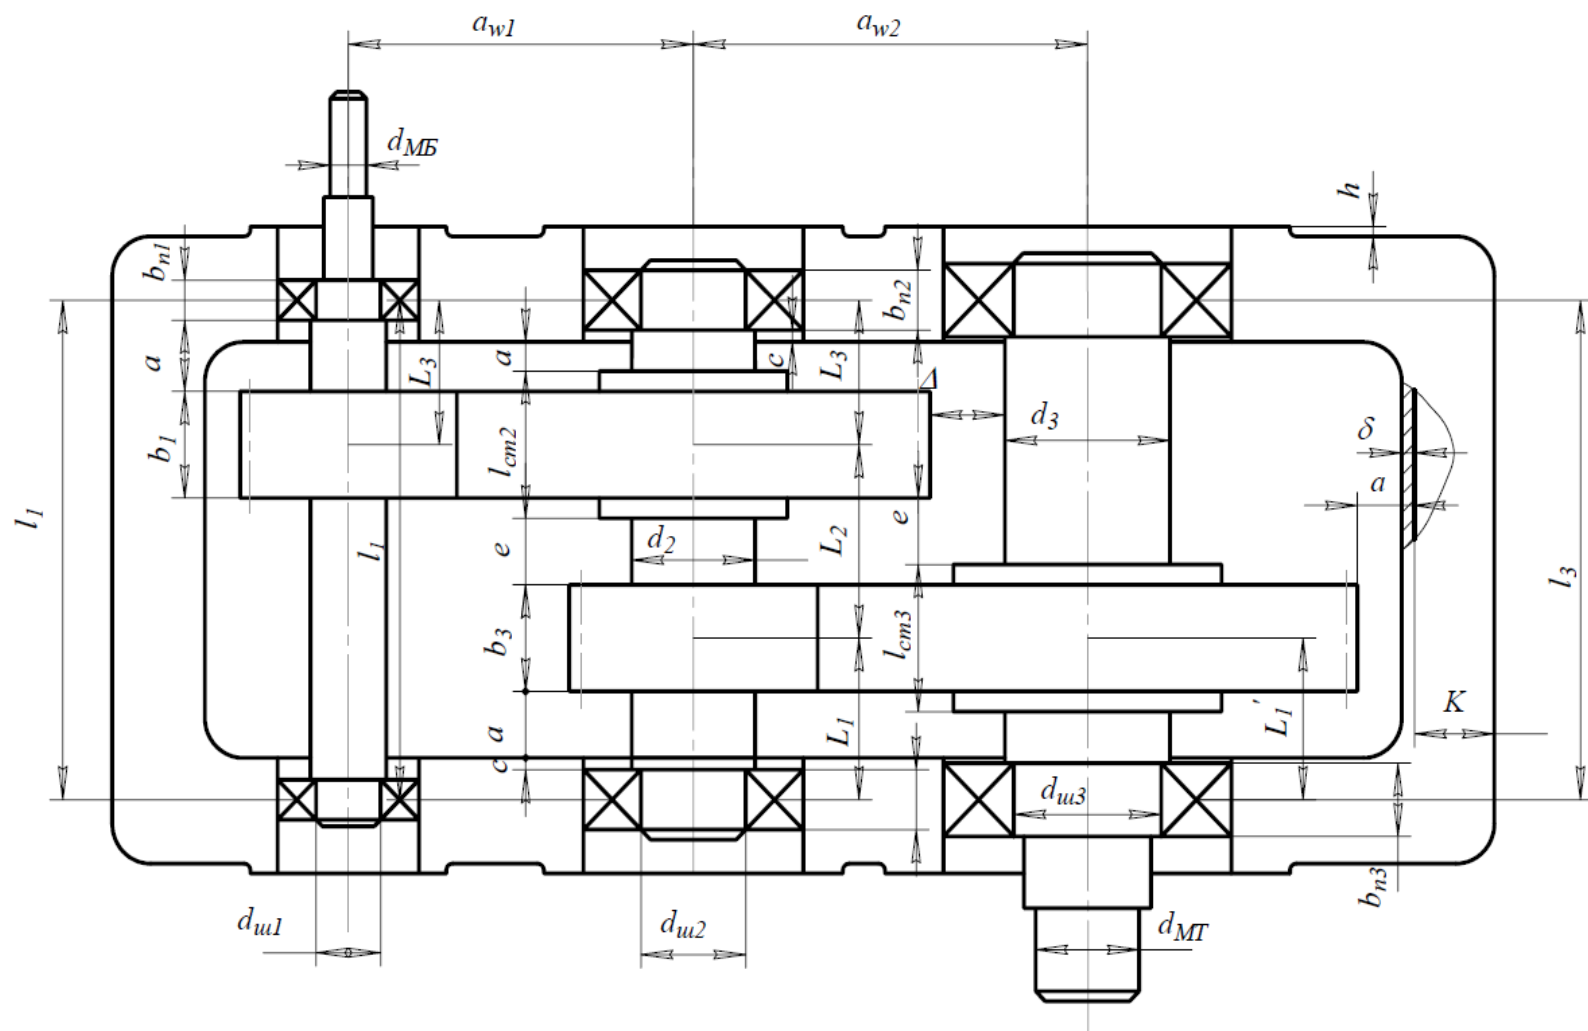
Эскизная компоновка двухступенчатого цилиндрического редуктора
